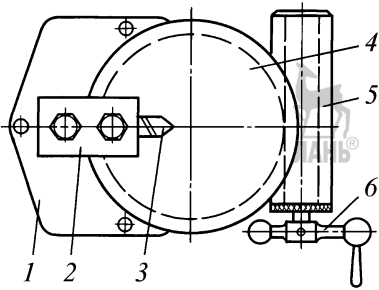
Поворотный стол для обработки сферических поверхностей:
